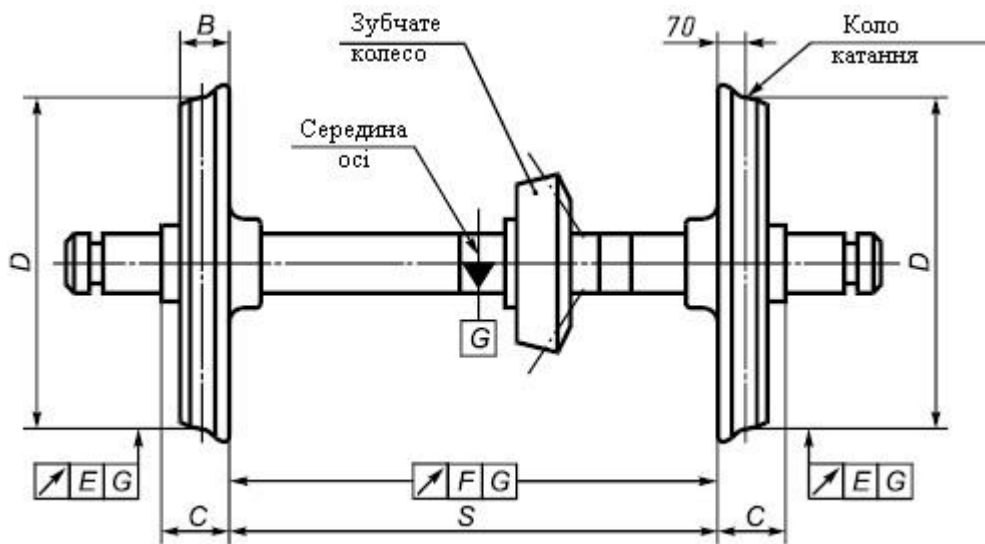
Колісна пара із зубчастим колесом осьового редуктора (привідна)
